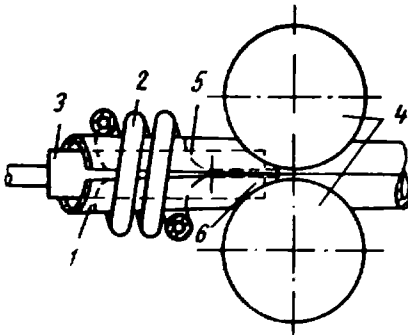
Схема высокочастотной сварки с индукционным подводом тока:
